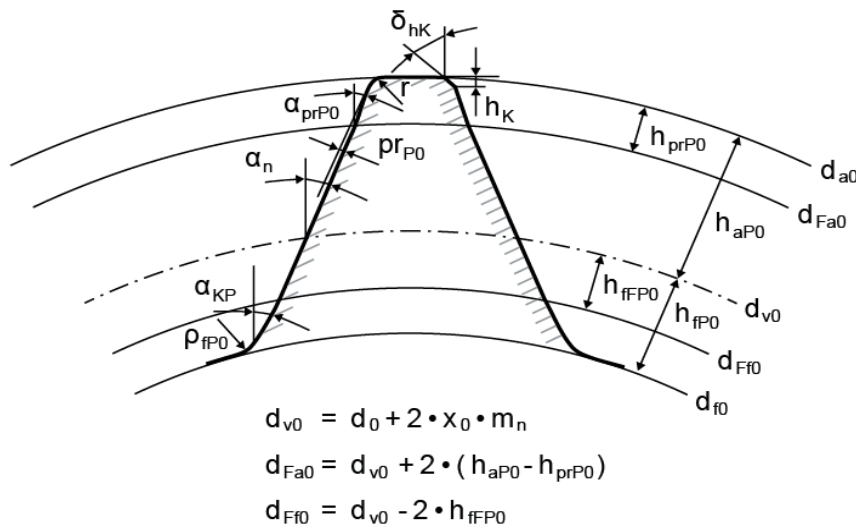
Bezugsprofil für die Konfiguration Werkzeug: Stossrad
